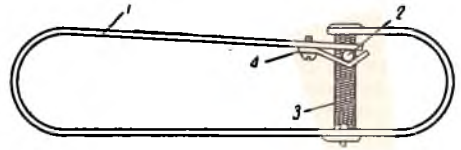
Искровая зажигалка для газа в виде металлической пружинящей скобы: 1 — корпус; 2 — кремь; 3 — огниво; 4 — пружинодержатель кремня
